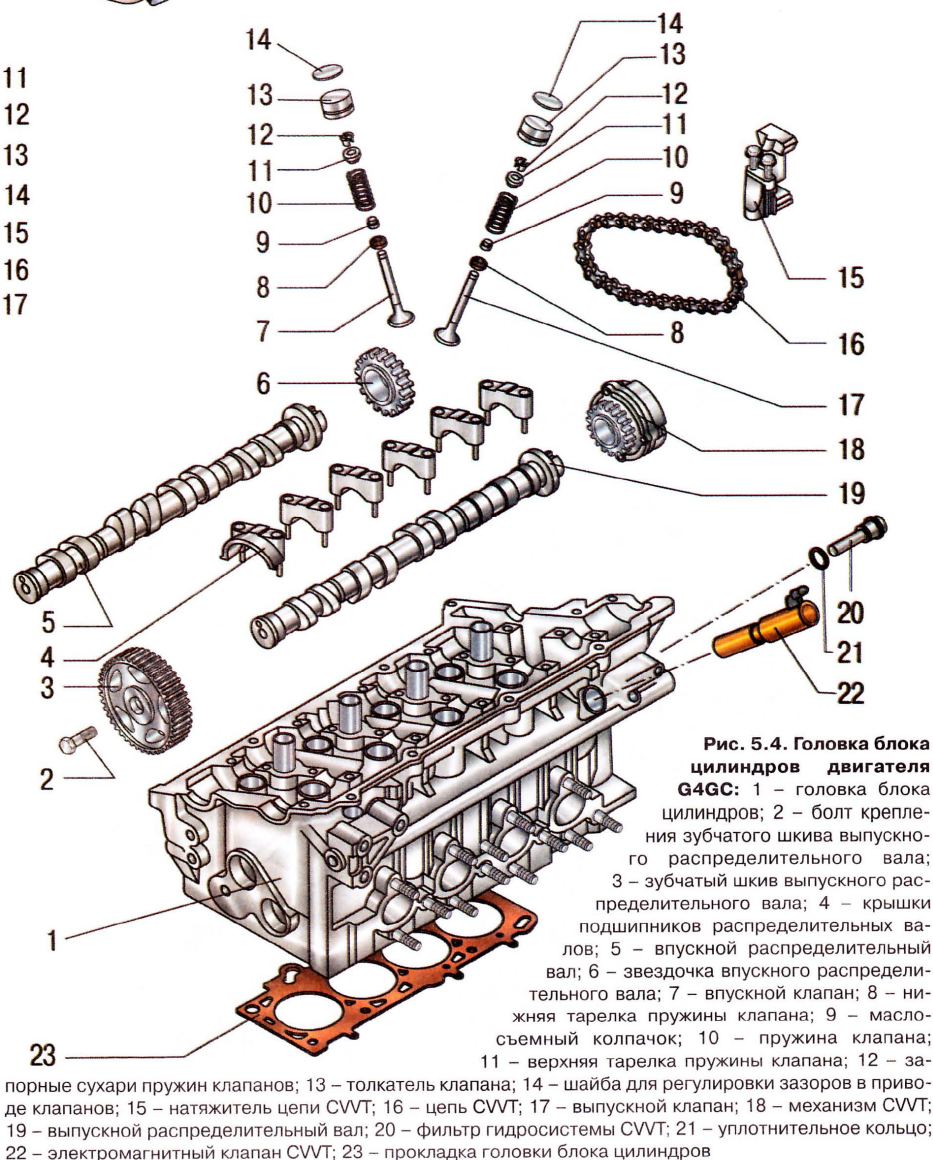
Головка блока цилиндров двигателя G4GC: 1 – головка блока цилиндров; 2 – болт крепления зубчатого шкива выпускного распределительного вала;
